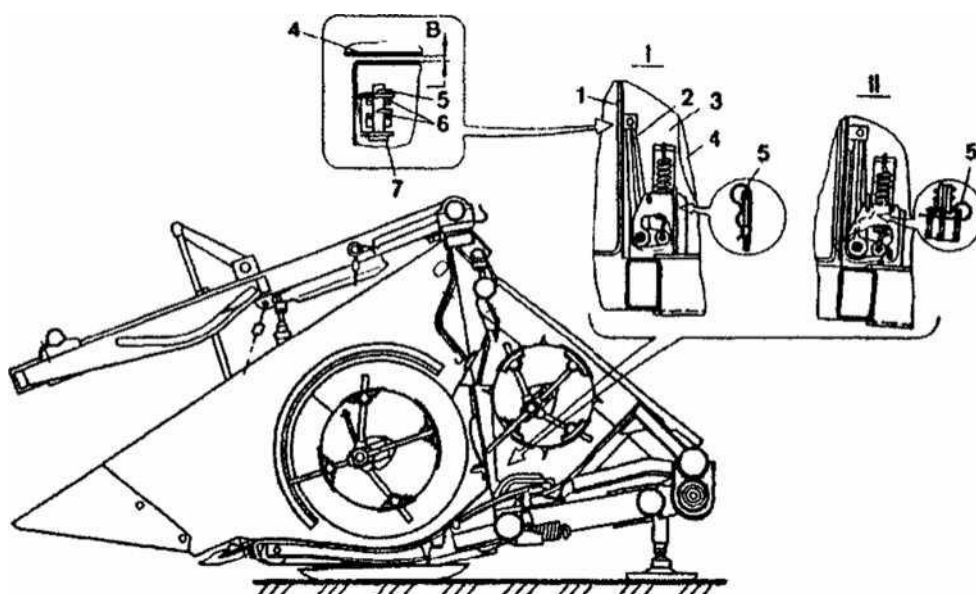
Жатка с боковым уплотнительным щитком:
